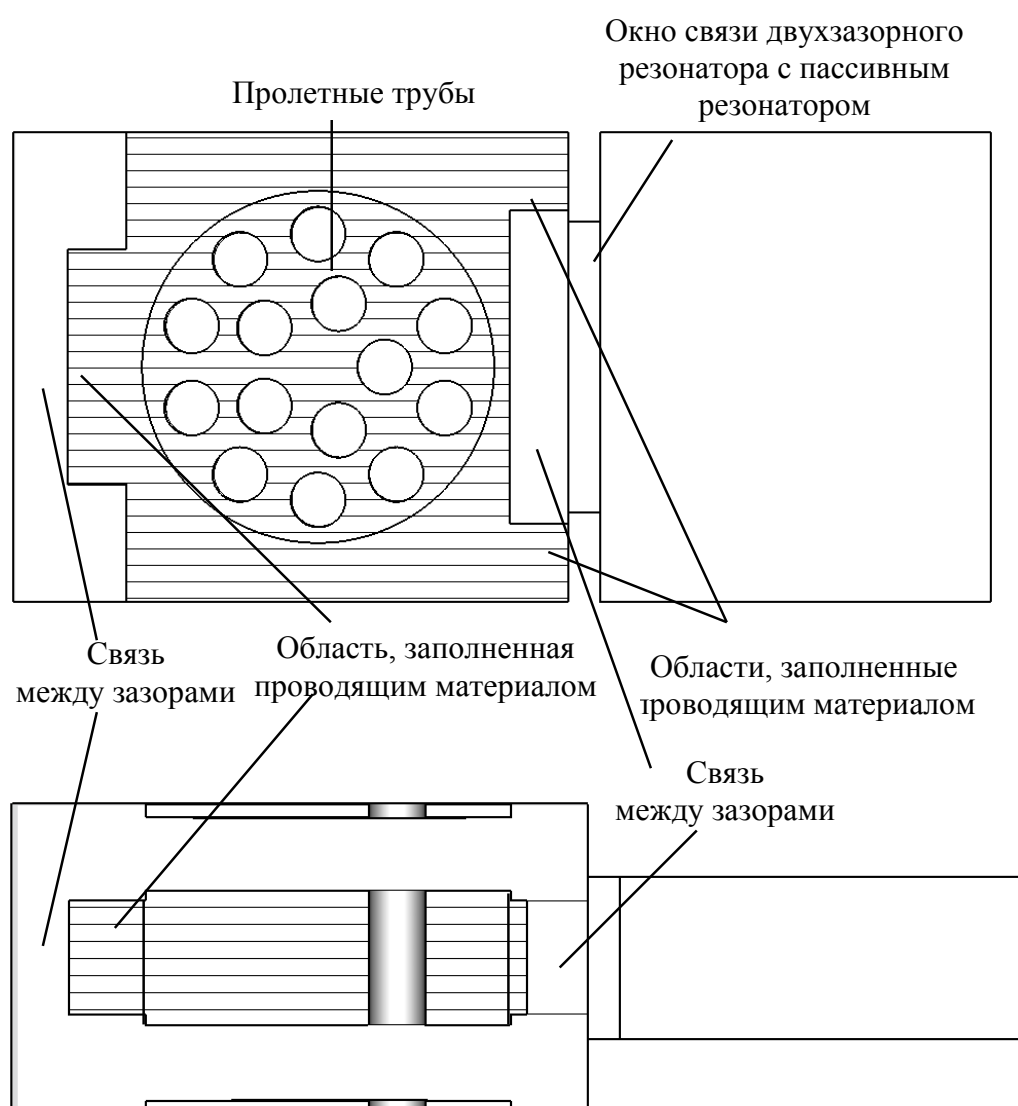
Конструкция двухзазорного резонатора с перемычкой, содержащей выступ и паз
